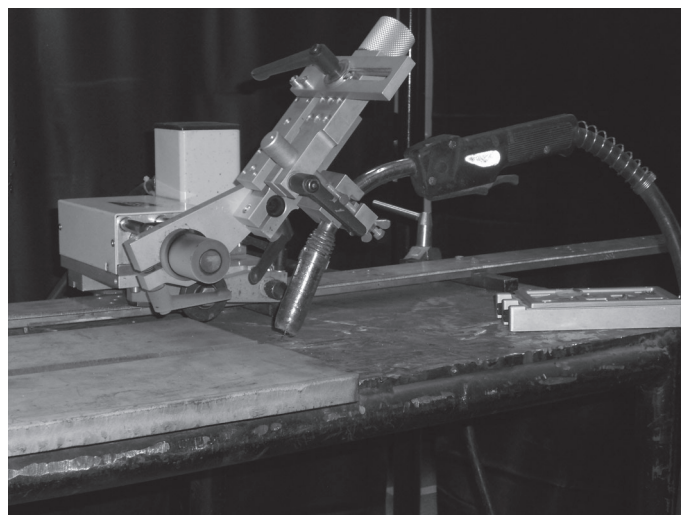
Montagem utilizada para soldagem dos corpos de prova.
